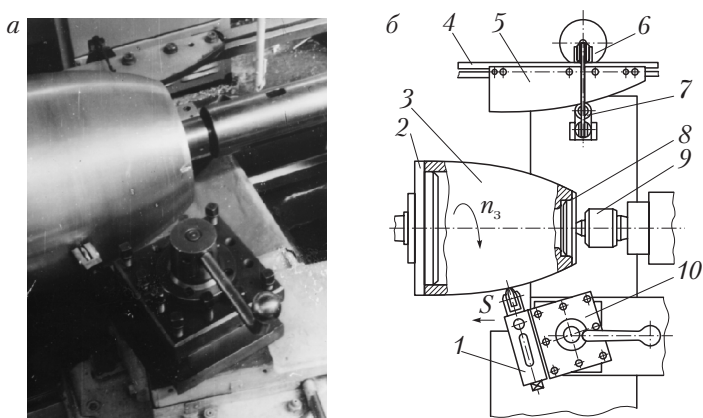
Вибронакатывание корпусов аппаратуры профильным роликом на установке, созданной на базе токарно-винторезного станка и оборудованной рамой с копирным устройством (а), и схема обработки ППД по копиру (б)
